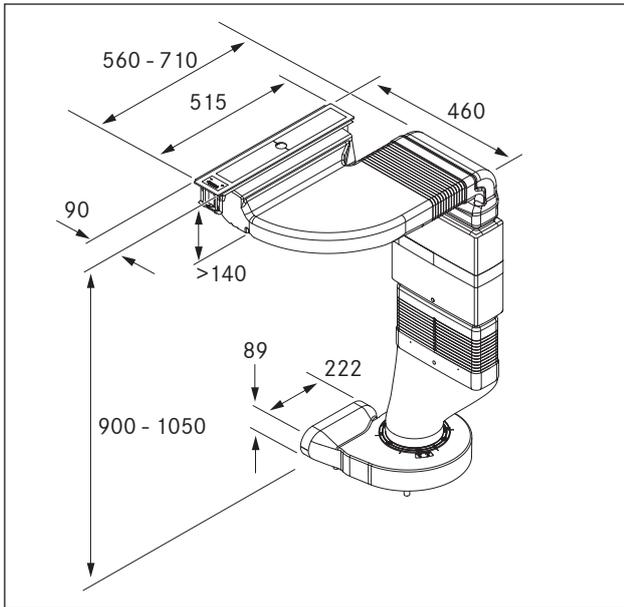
Dimensiones del aparato con pieza de empalme acodada
